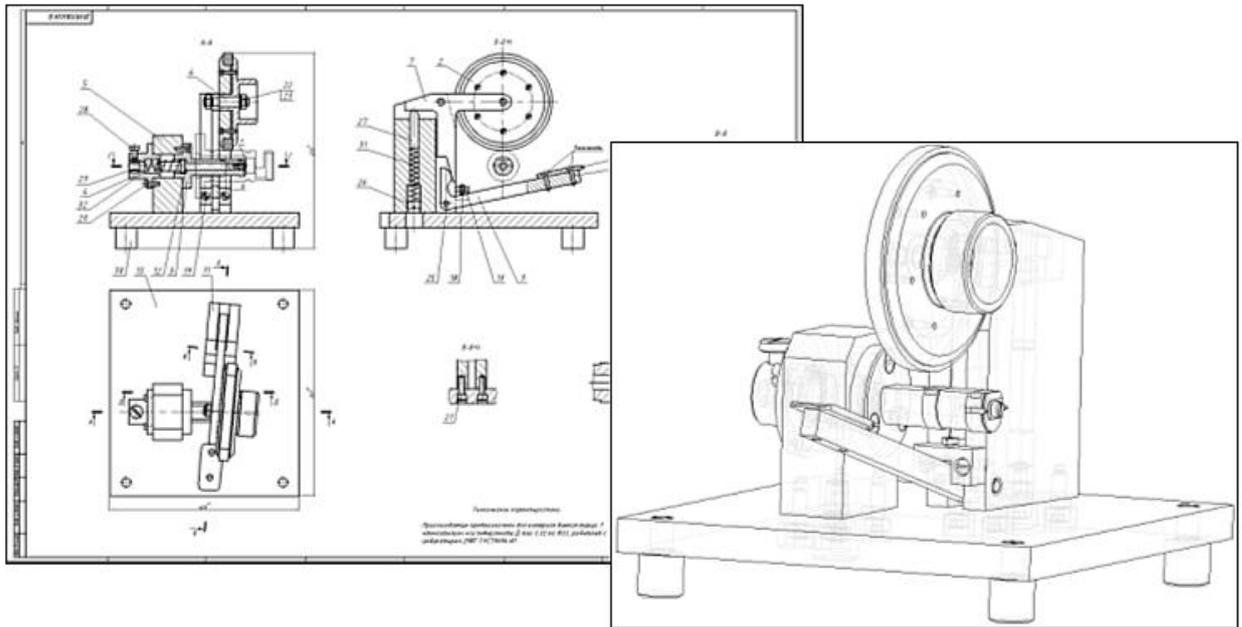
3D модель приспособления и сборочный чертеж, созданные в САД
